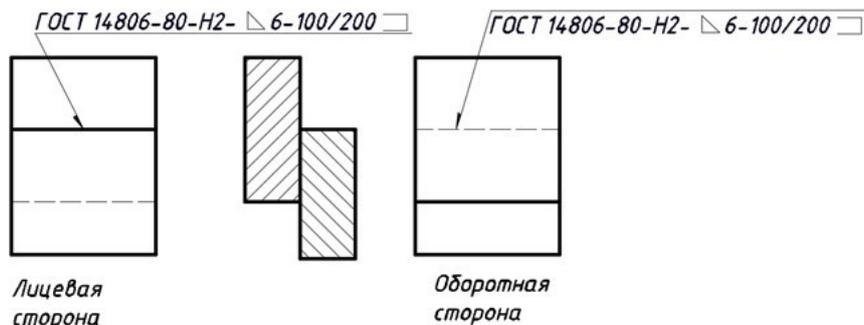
Образец условного обозначения сварного шва.
